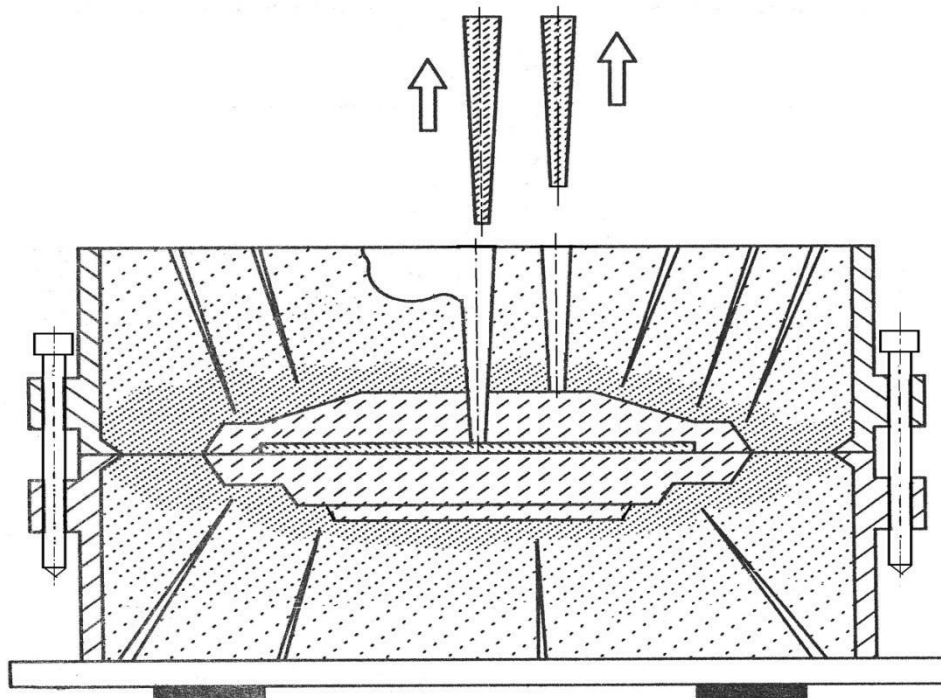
Zaformovaný model s vtokovou soustavou v dělené formě
